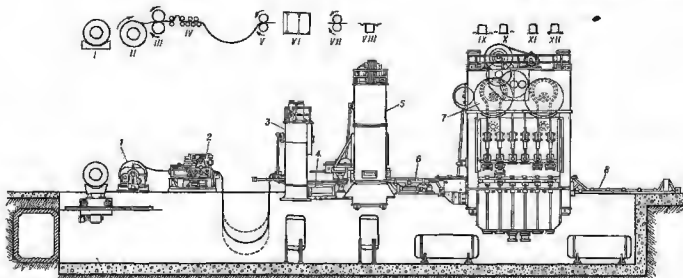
Схема автоматизированной линии для штамповки нагретого двигателя: I — исходное положение рудона сталовой ленты; II — разогрев; III — очистка; IV — протравка; V — подача; VI — выработка заготовки; VII — охлаждение; VIII — вытяжка изделия; IX — переформовка изделия и правка фланцев; X — обкатка фланцев по контуру; XI — формовка обкатки жесткостью и фланцами по контуру; XII — обработка отверстий; 1 — раздаточное устройство; 2 — дисперсионная машина; 3 — дуговой электропрес с арговым действием с плазменной подачей; 4 — механизм передачи и подъемный стол заготовок; 5 — одноканальный прес с арговым действием для вытяжки; 6 — механизм передачи изделий и смена штампа; 7 — электропрес с арговым действием; 8 — механизм транспортирования изделий в штамп.
